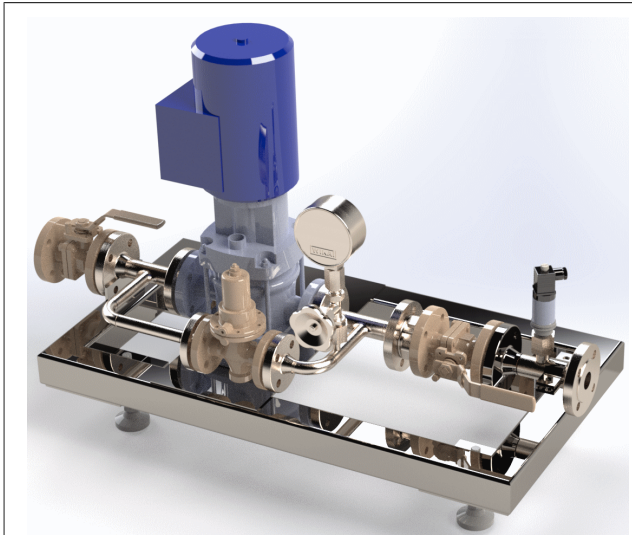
Ausführung Pumpenbaugruppe Typ 7111-1
